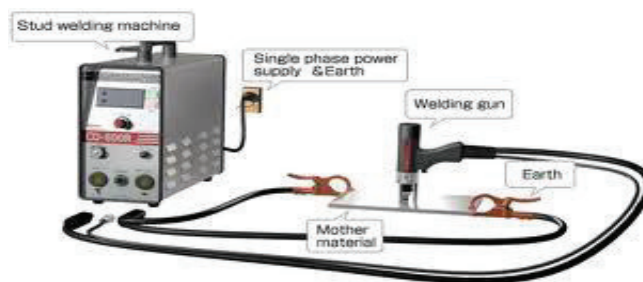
ARC Stud Welding ⁽⁷⁾
